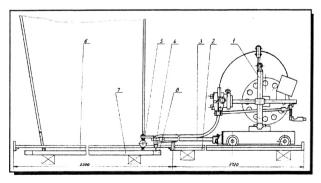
Общий вид модернизированного трактора и схема выполнения сварных швов нижнего яруса
